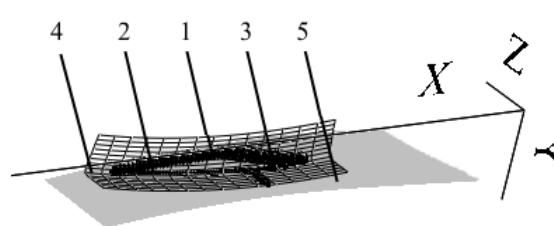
Пляма контакту фрези й кулачка розподільчого вала при обробці ділянки кулачка найбільшого радіуса
